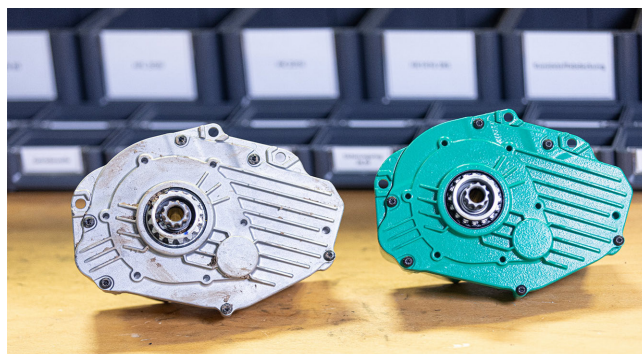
Gebrauchter und aufgearbeiteter Elektrofahrradmotor.
